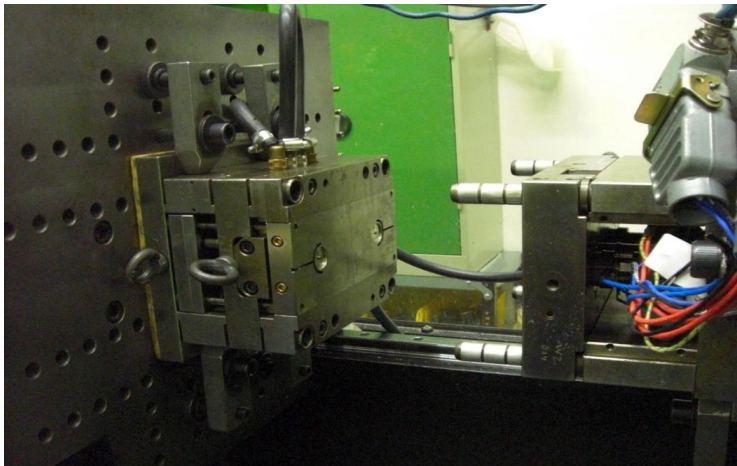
Untersuchung der beschichteten Heißkanaldüsen im Spritzgießprozess, Werkzeug um 90° gedreht.
